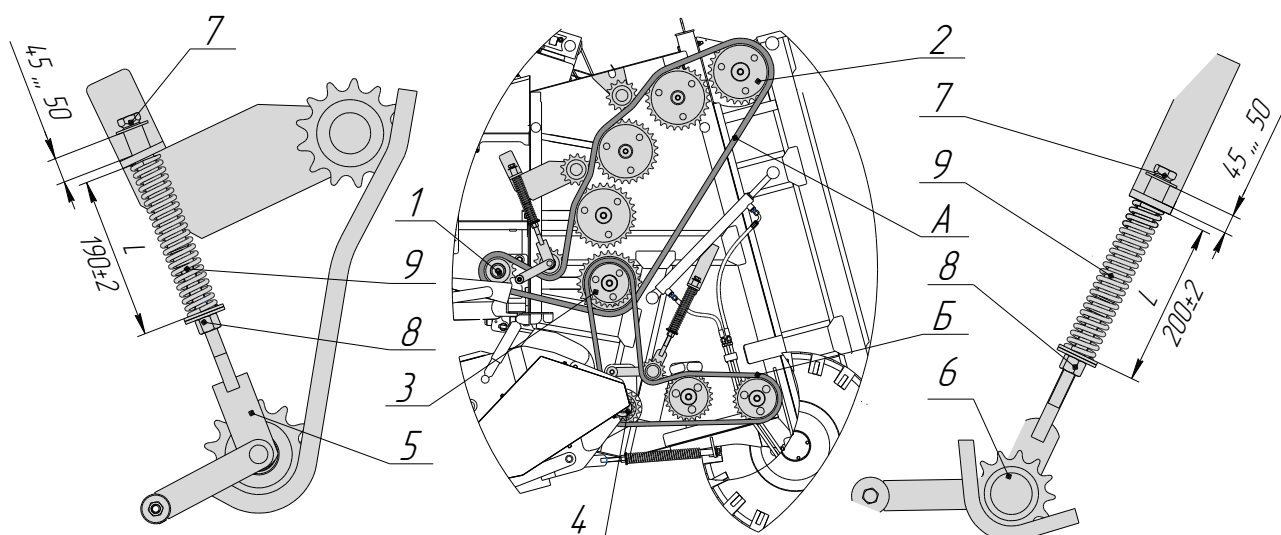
Регулировка натяжения цепей передней камеры: «А» - Привод левый верхний; «Б» - Привод левый нижний; 1 – звездочка привода «А»; 2 – звездочка с вальцом привода цепи задней камеры; 3 – двойная звездочка привода «Б»; 4 – вал привода подборщика и подавателя; 5 – натяжитель контура «А»; 6 – натяжитель контура «Б»; 7 – направляющий винт; 8 – гайка натяжителя; 9 – пружина натяжителя.
